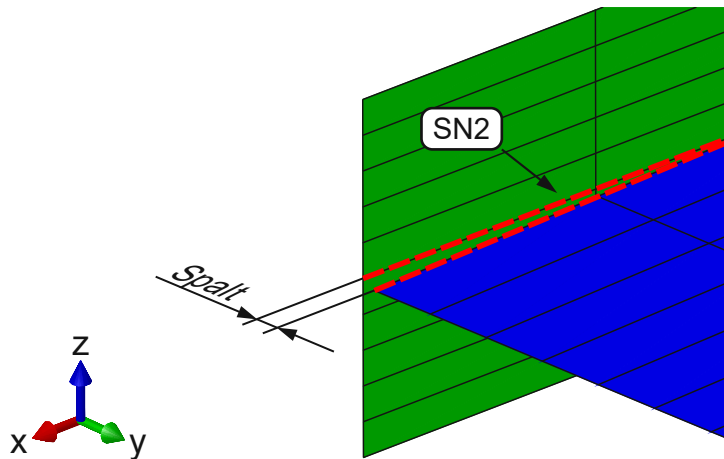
Auswirkungen des Schweißverzugs beim sequenziellen Schweißen:
